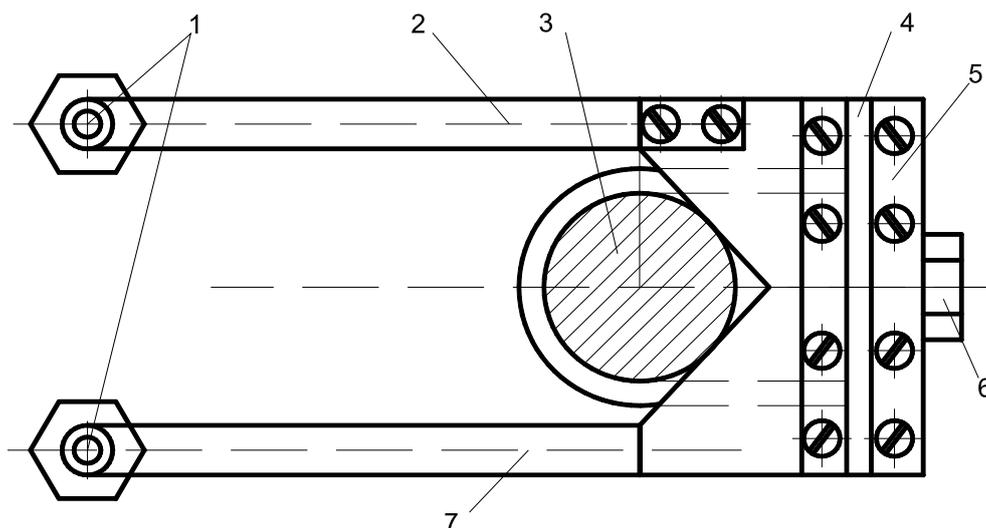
Деформометр: вид сверху: 1 – места подвешивания тяг; 2 – верхний кронштейн; 3 – испытуемый образец; 4 – гибкая пластина; 5 – корпус деформометра; 6 – винт крепления пружины; 7 – нижний кронштейн
